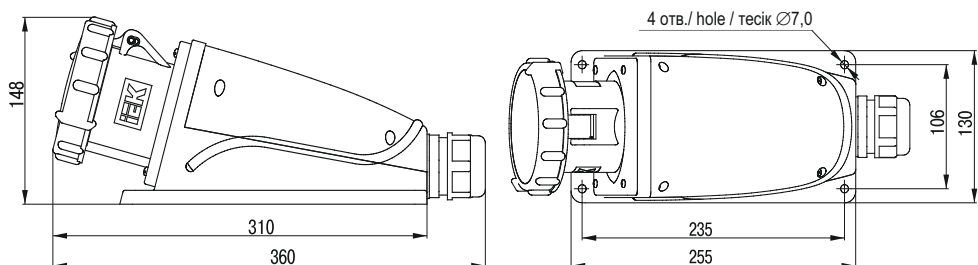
Габаритные размеры соединителей типа ССИ-133, ССИ-134, ССИ-135 / Figure 8 – Overall dimensions of plug and socket-outlets SSI-133, SSI-134, SSI-135 / Сурет 8 – ССИ-133, ССИ-134, ССИ-135 типті жалғастырғыштардың габариттік өлшемдері
